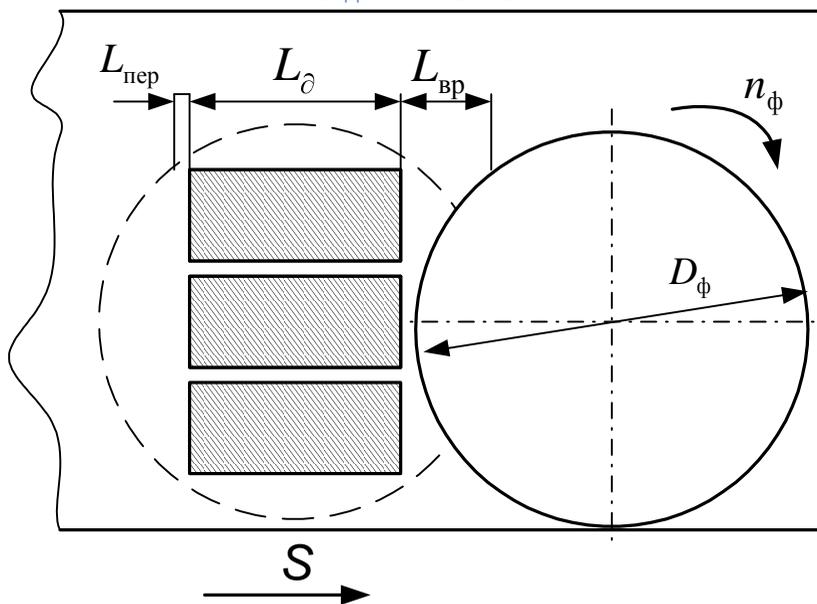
Схема параллельного фрезерования плоскости торцевой фрезой на трех заготовках
